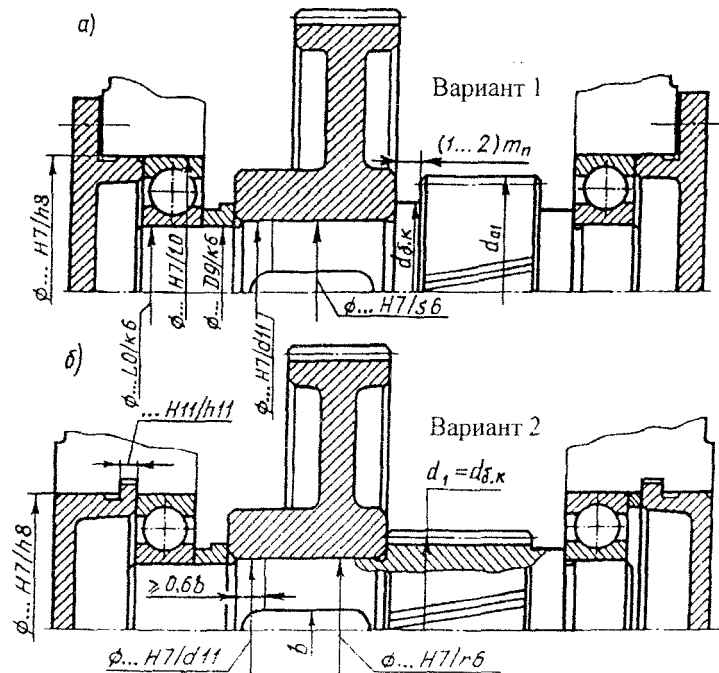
Варианты конструкции промежуточного вала двухступенчатого цилиндрического редуктора, выполненного по простой развернутой схеме: $d_{δ.к}$ - диаметр буртика вала для упора ступицы колеса
